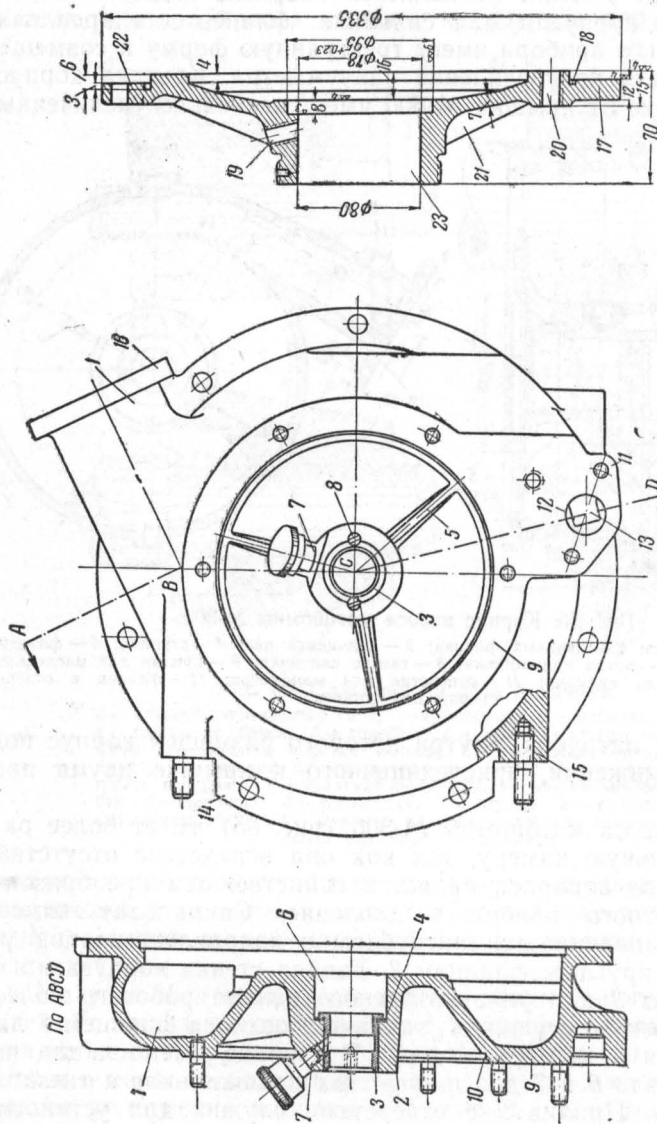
Корпус и крышка насоса мотопомпы М-600.
